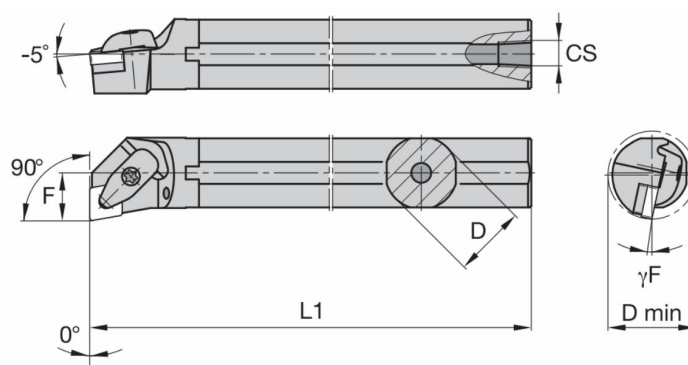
Токарный проходной резец (для внутренней обработки)
